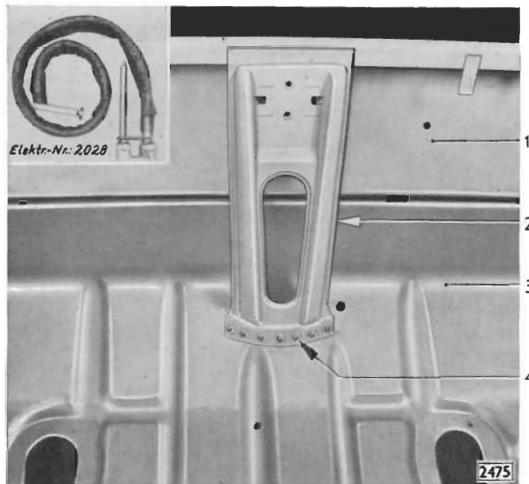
Stütze der Kofferraumrückwand an Bodenblech stoßpunktgeschweißt
